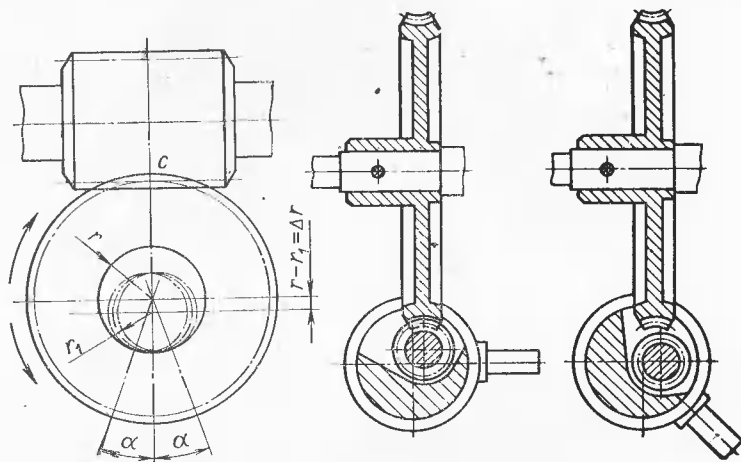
Радиальный зазор в подшипниках червячного колеса
